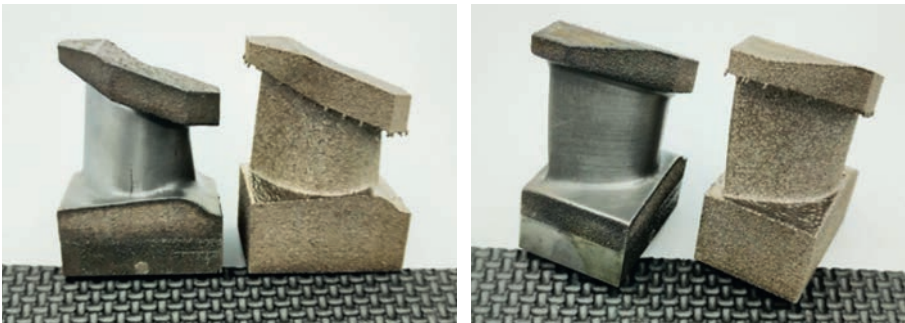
Лопатки турбины и заготовки АП (СЭЛП)
